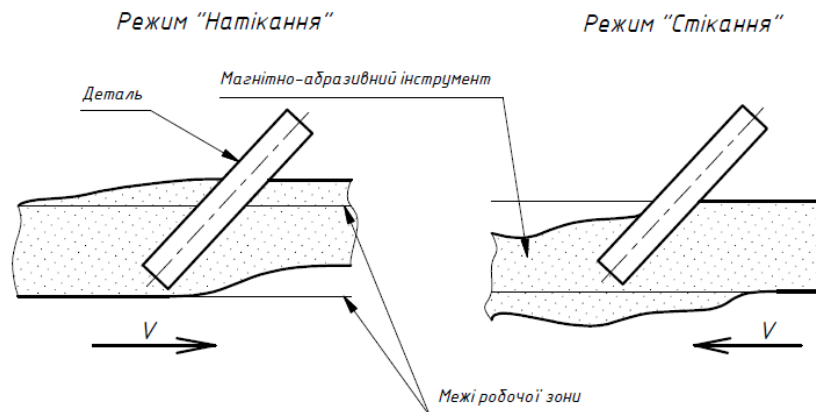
Схеми розташування деталей при МАО в кільцевому робочому зазорі
